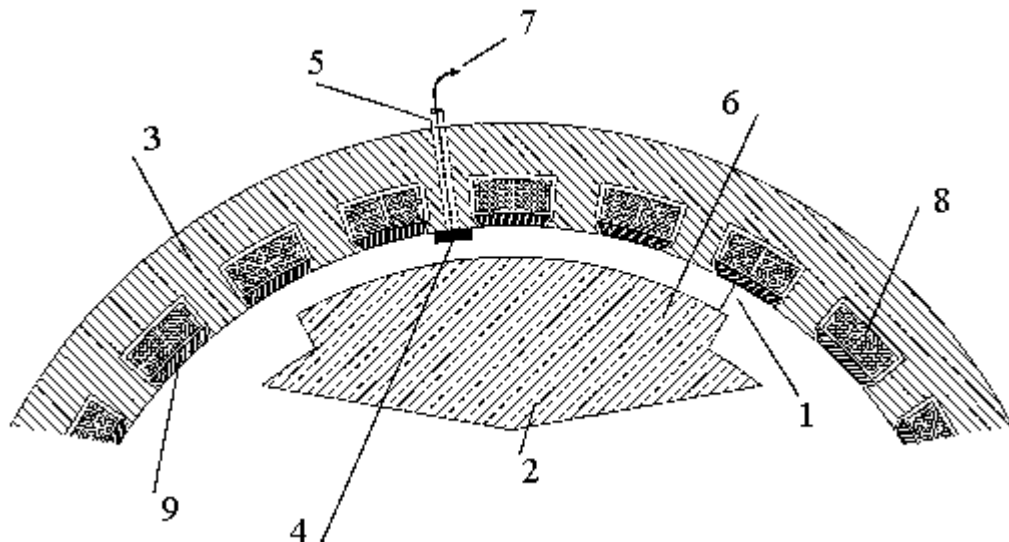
13. Конструктивні особливості розташування датчика в робочому зазорі гідрогенератора: 1 – робочий зазор; 2 – ротор; 3 – статор; 4 – датчик; 5 – захистна оболонка; 6 – полюс ротора; 7 – кабель приєднання; 8 – обмотка статора; 9 – фіксуючий клин пазу.
